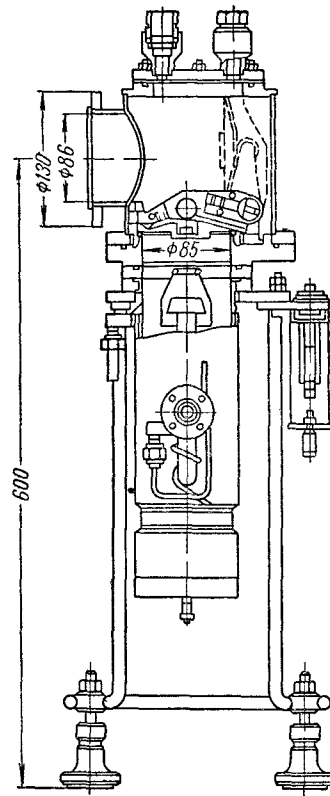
Схема вакуумного агрегата ВА-01-1.
